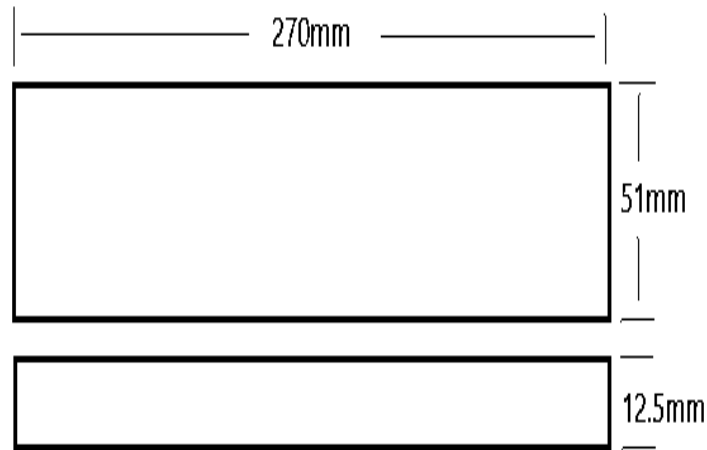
Caracterización dimensional para ensayo de flexión. Fuente: Elaboración propia.
